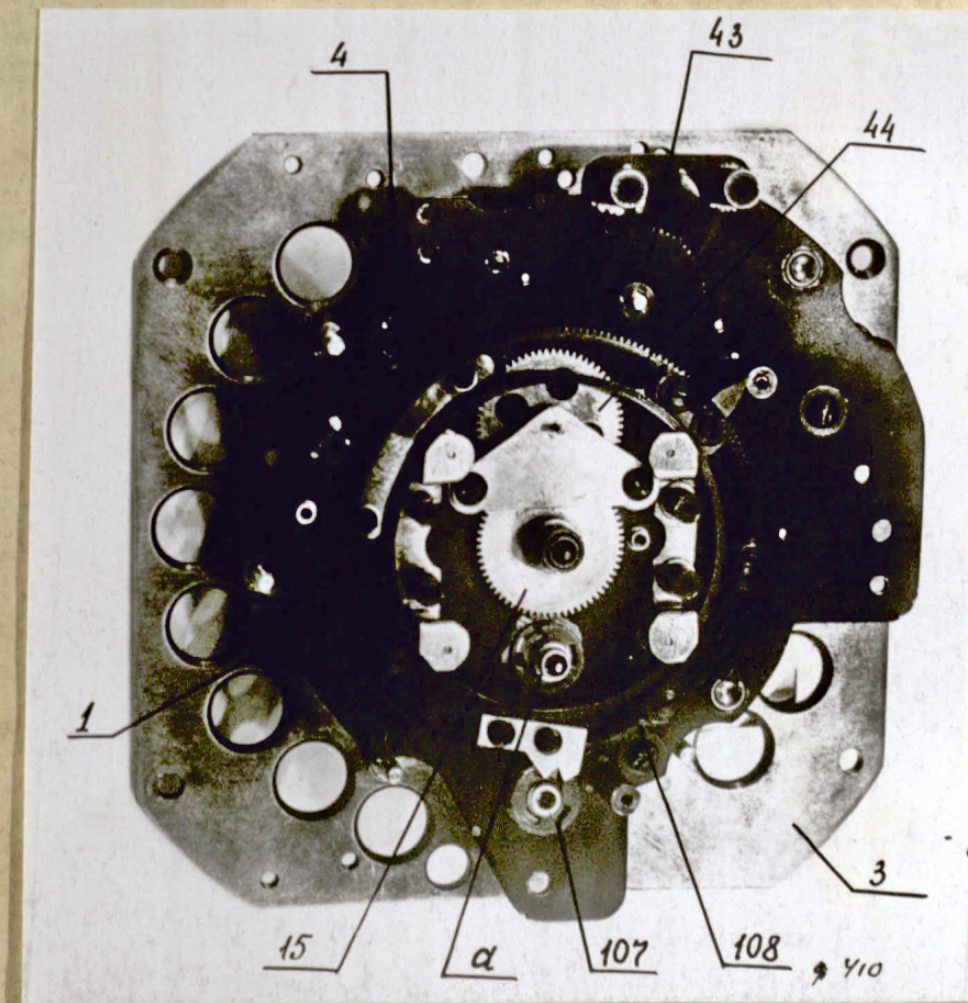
Вид на прибор ИВК2А со снятыми шкалами
